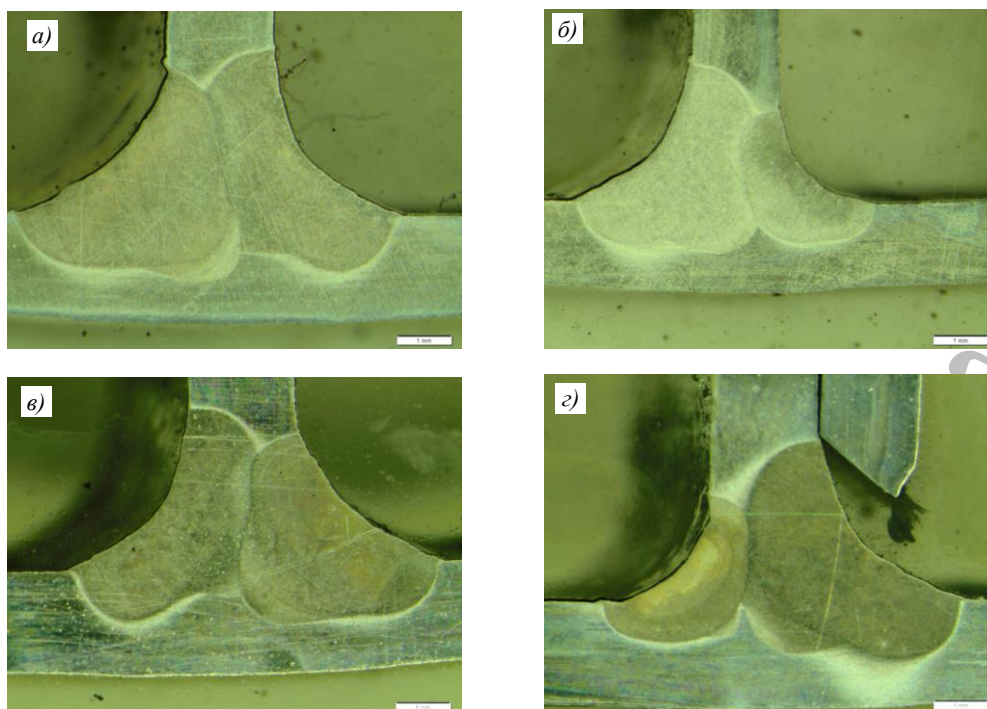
Макроструктура сварных тавровых соединений, выполненных лазерной сваркой по режимам I (а, б) и II (в, г) и лазерной сваркой с подваркой (б, г)
